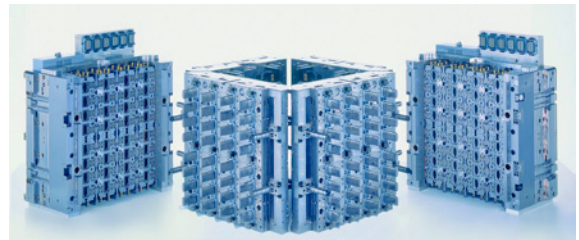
Etagenwendewerkzeug (Quelle: FOBOHA GmbH)
